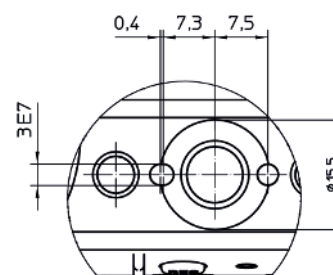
Hi-5 : dettaglio vista dall'alto Z
